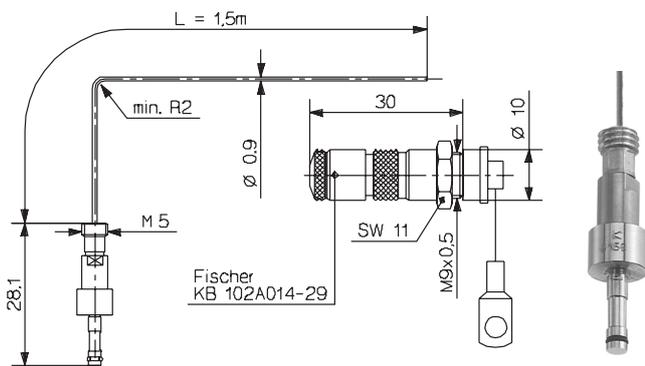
Alternative Ausführung des Sensors Typ 6159A... mit Single-Wire-Technik
